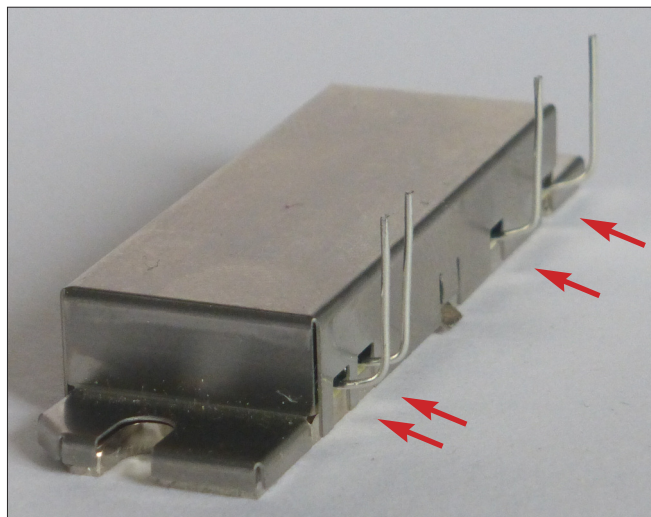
Die Anschlüsse des Powermoduls sind mit einer Rundzange so zu biegen, dass keine Kraft auf die Lötunkte im Innern ausgeübt wird.
